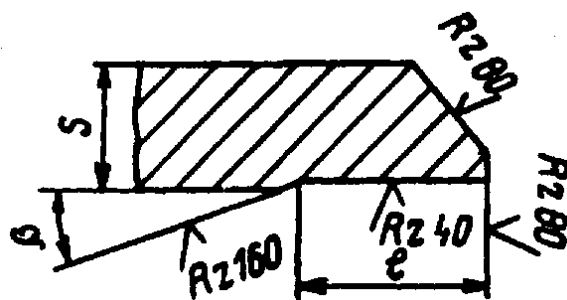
Шероховатость трубных заготовок перед сборкой и сваркой паропровода
